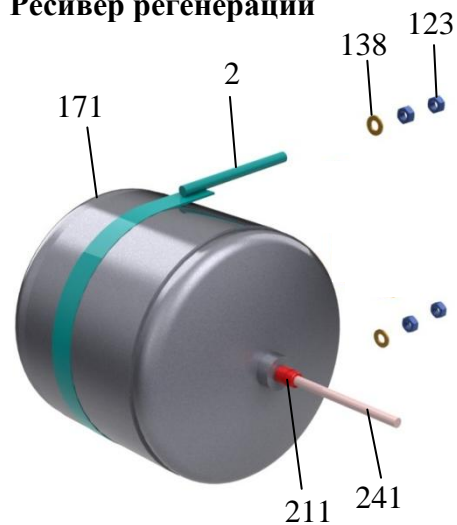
(лист 2 из 2) – Установка ресиверов
